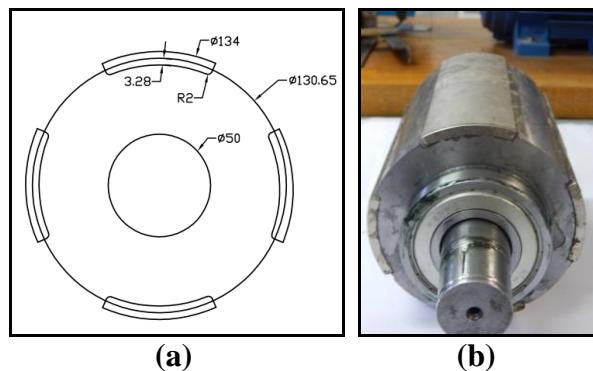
Rotor de polos lisos – (a) Desenho esquemático – (b) rotor montado [6]
